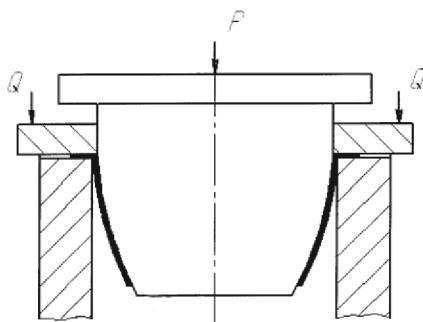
Схема отбортовки в инструментальном штампе тонкостенных заготовок
